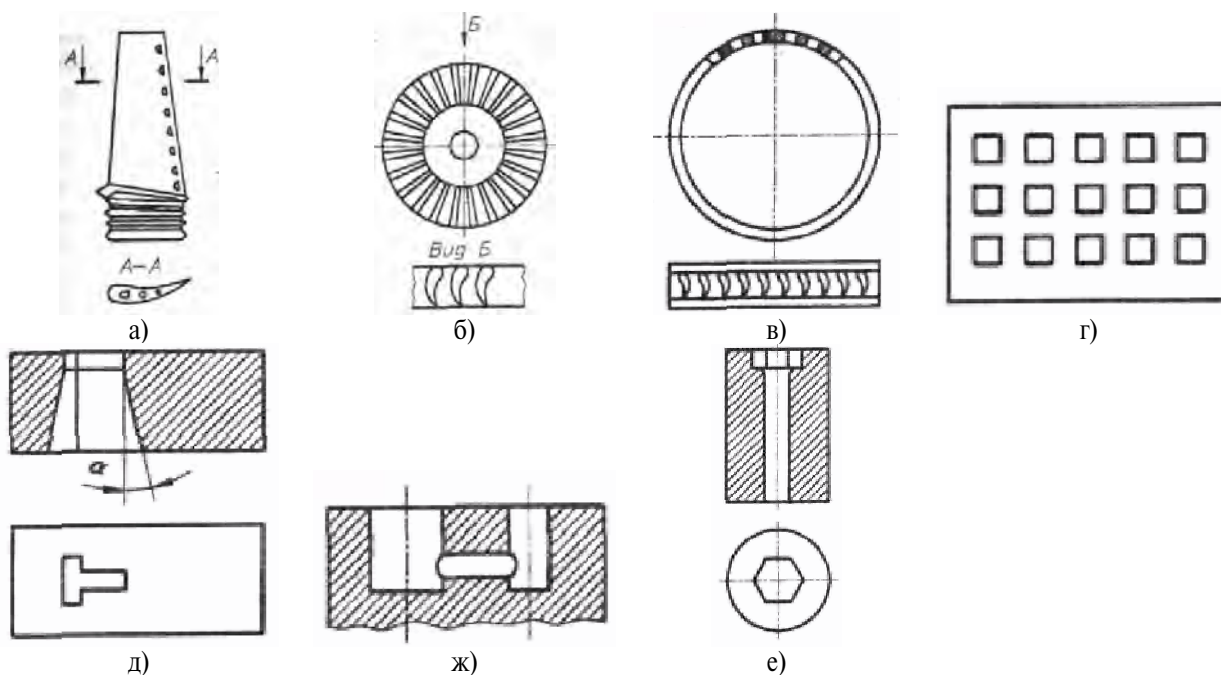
Примеры прошивания некруглых отверстий и пазов:
